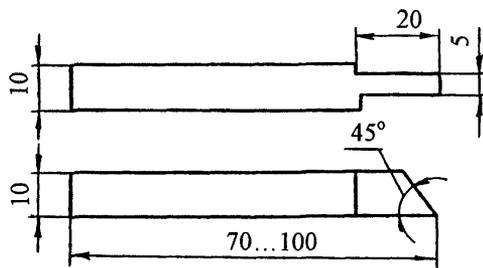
Боек для изготовления искусственных дефектов типа зарубок
